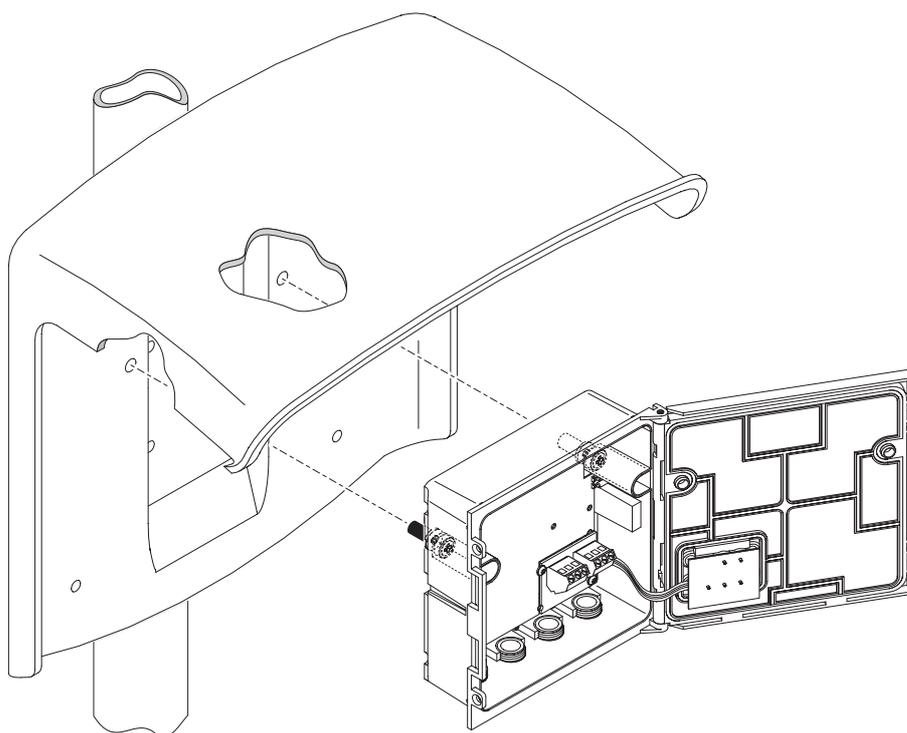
Modul am Schutzdach SSH/IQ montieren
